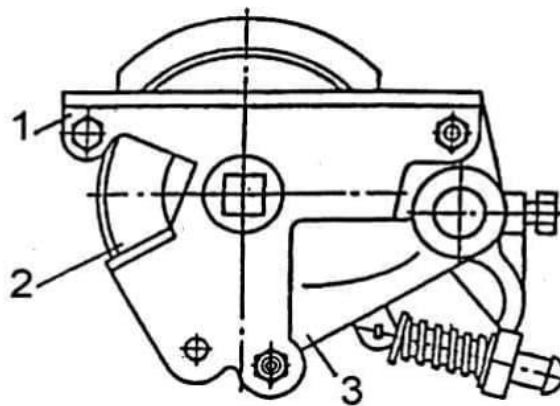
Конструкція внутрішньо реберчастого висівного апарату сівалки СРВ-3,6: 1- коробка; 2-кільце для висіва; 3- клапанний механізм
